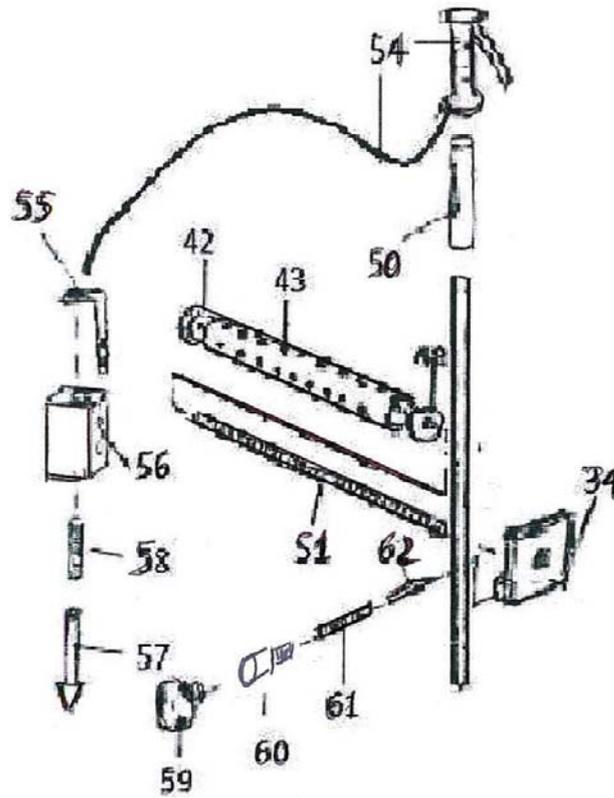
Ersatzteilzeichnung 4 Langlochbohrmaschine LLB 30
